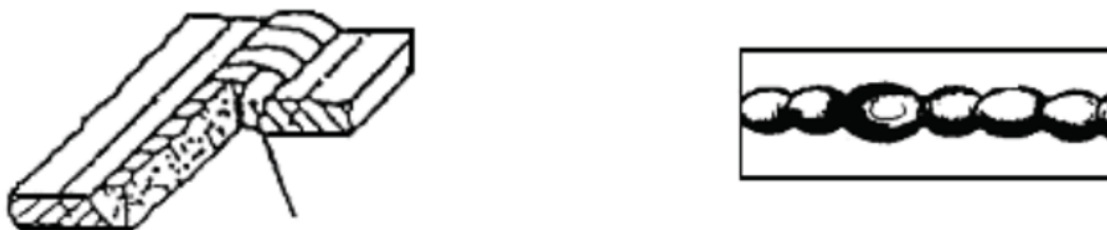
Эскиз дефекта сварного шва
